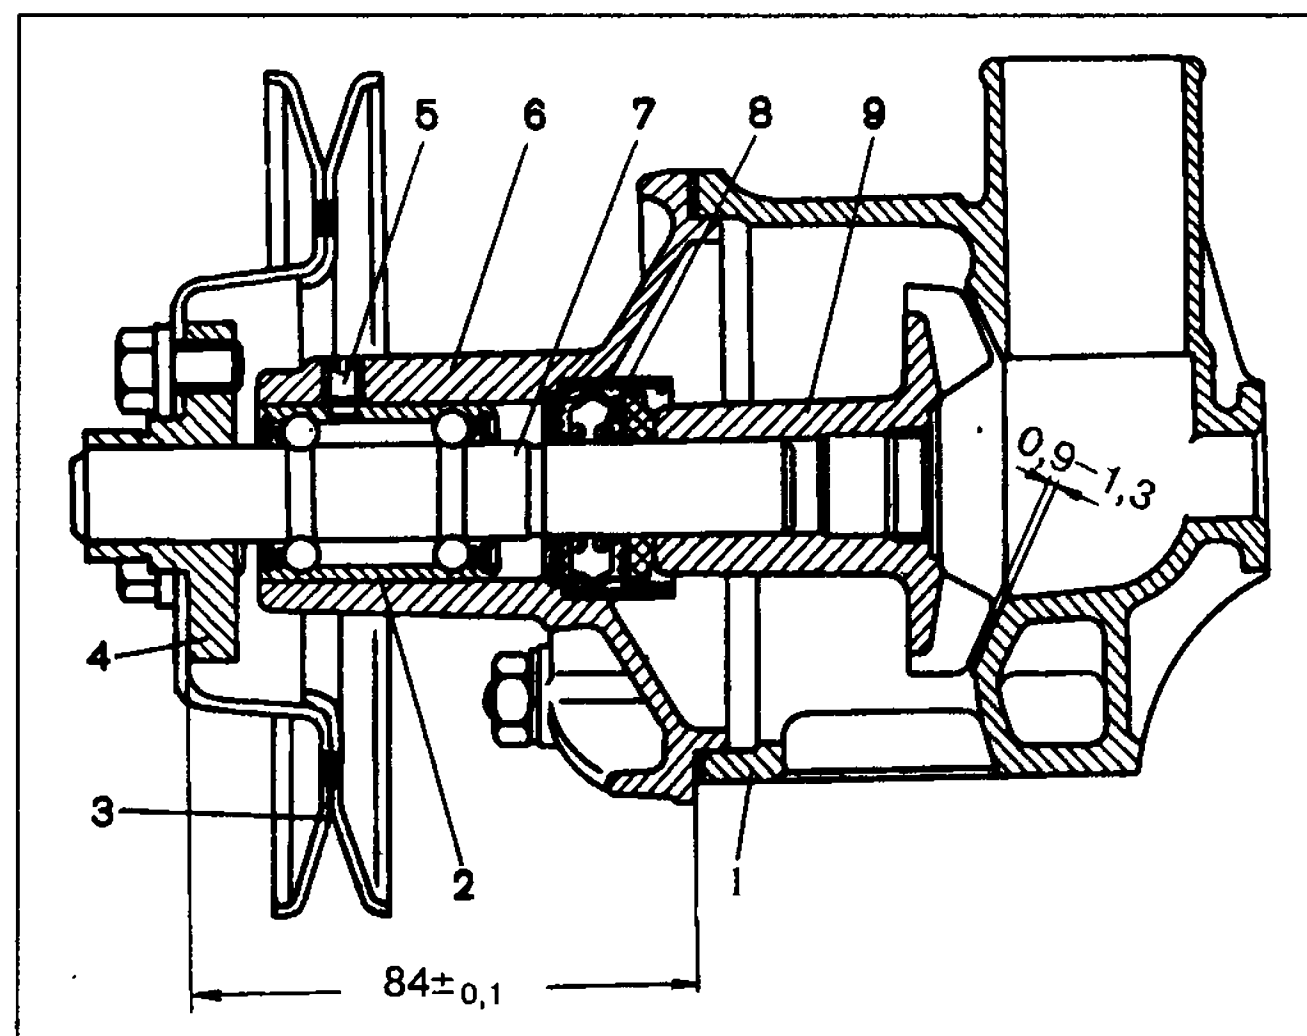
Продольный разрез насоса охлаждающей жидкости: 1 - корпус; 2 - подшипник; 3 - шкив; 4 - ступица шкива; 5 - стопорный винт подшипника; 6 - крышка; 7 - валик; 8 - сальник; 9 - крыльчатка
